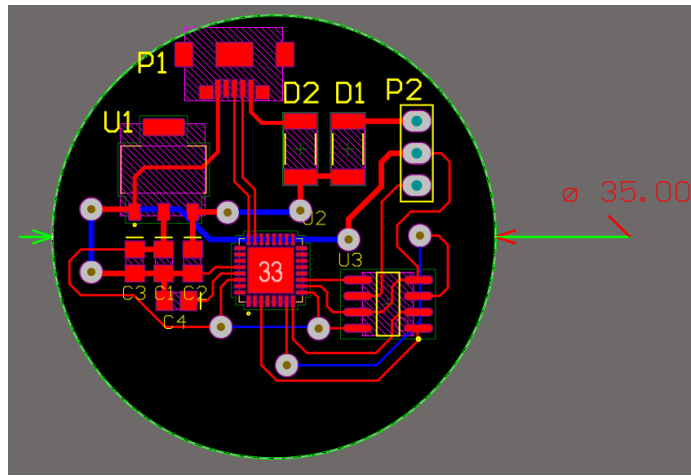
Prototipo PCB del módulo estimulador con SAM21 encapsulado QFN.
